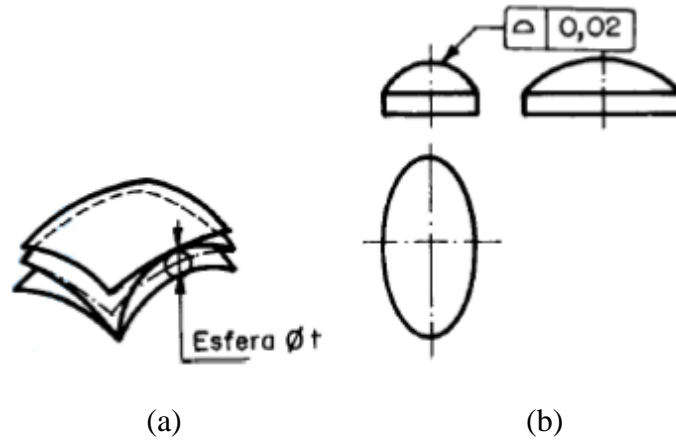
(a) Superfícies regadas pelo diâmetro “t”; (b) indicação da tolerância no desenho técnico. (Adaptado de: NBR 6809)
